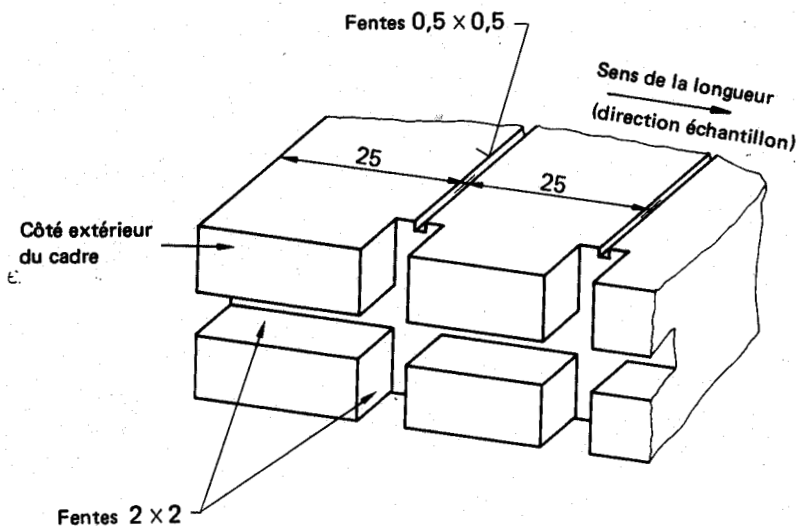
Exemple de section du cadre en forme de U, partie inférieure prévue pour équipement avec fils de support
